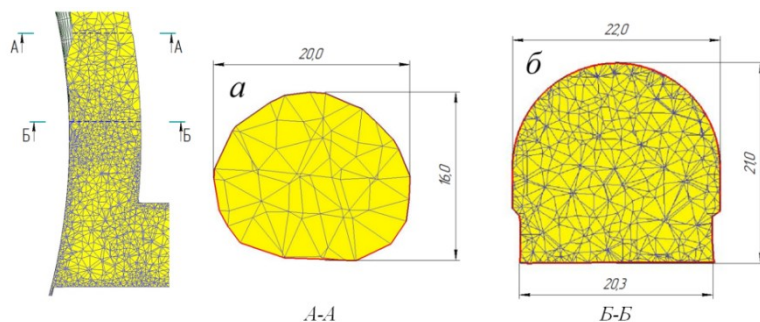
Распрессовка заготовки перед переходом в форкамеру:
